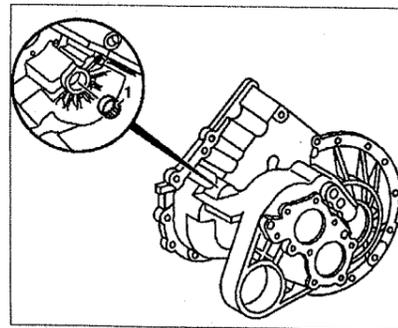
Снятие и установка игольчатого подшипника 1 вала передачи заднего хода.
